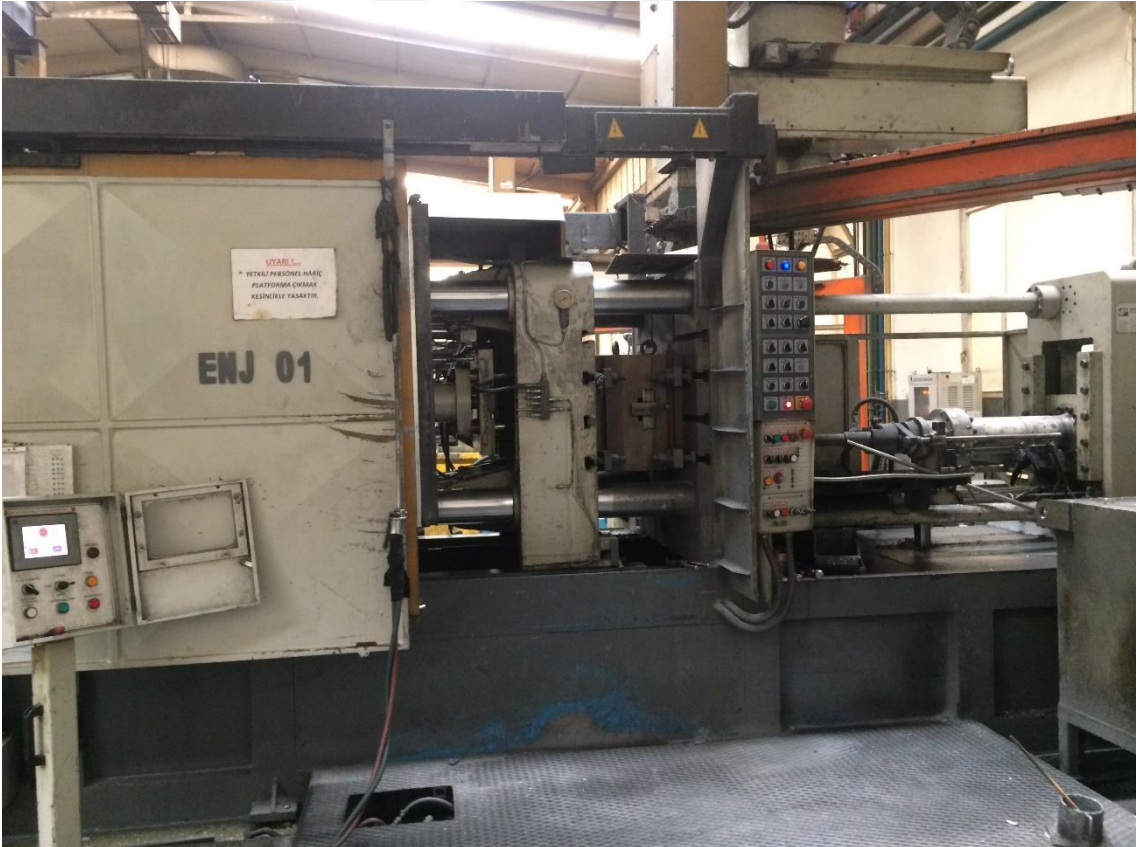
Soğuk kamaralı yüksek basınçlı döküm makinesi
